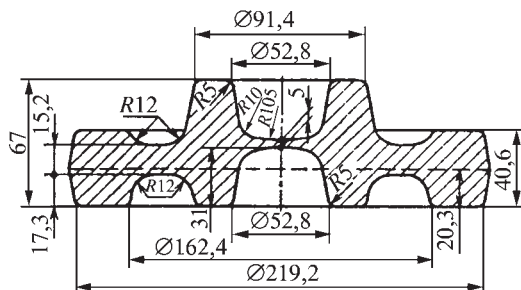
Чертеж поковки шестерни для изготовления штампа
